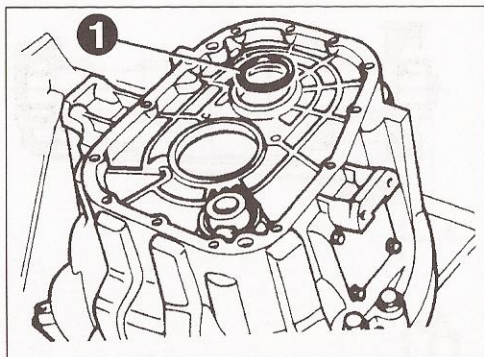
Установка регулировочного кольца (поз. 1) промежуточного вала.
